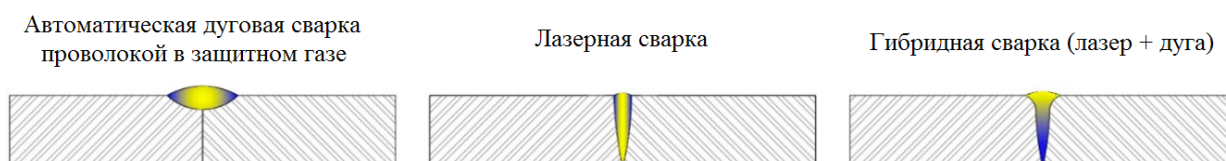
Поперечное сечение сварных швов, соединенных различными способами сварки: GMAW, LBW и LAHW [31]
